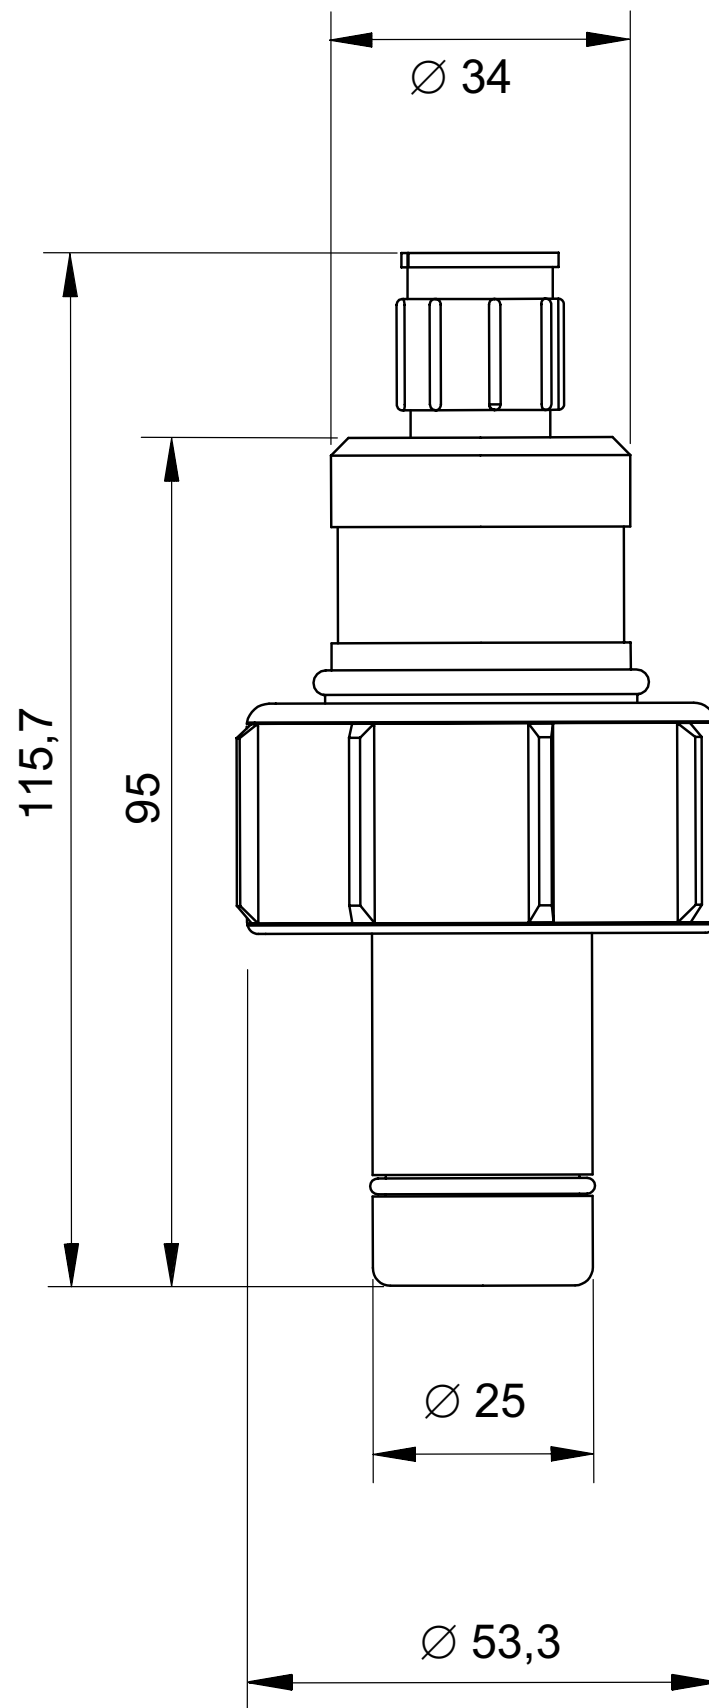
Desenho das dimensões do InPro 7100-25/7104-25 com 4 eletrodos
